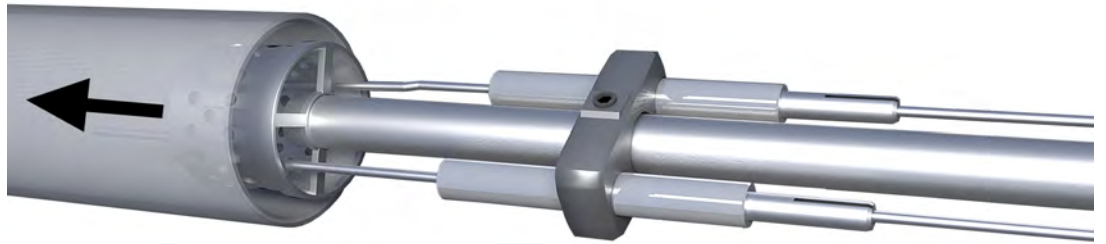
Etape 1 Remplacer les pièces d'usure du brûleur d'allumage
